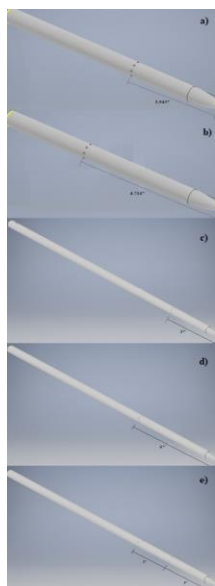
a) Diseño I; b) Diseño II; c) Diseño III; d) Diseño IV; e) Diseño V.
